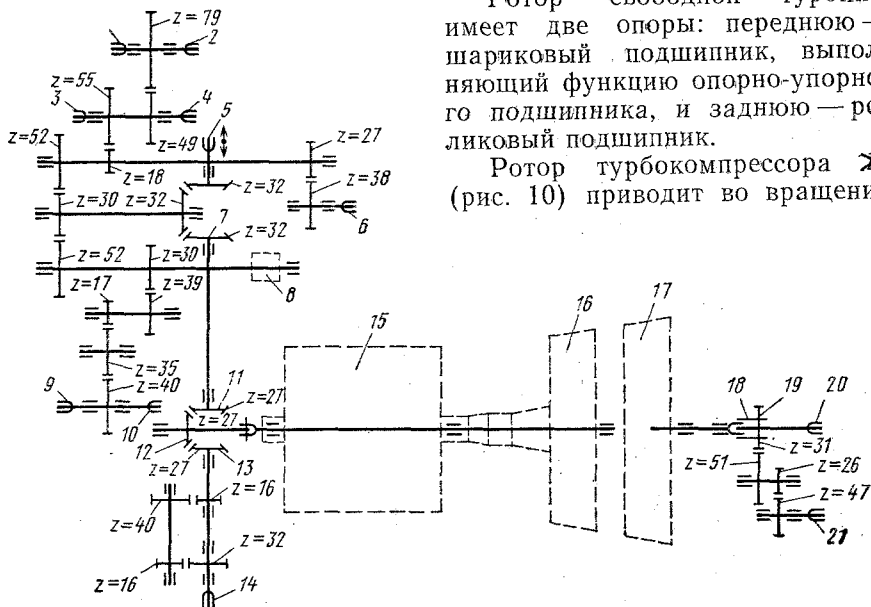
Кинематическая схема двигателя и приводов агрегатов:
